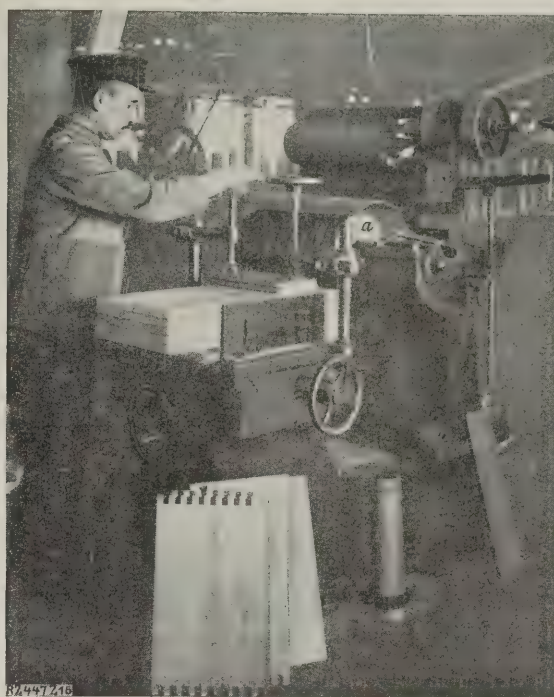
Zinkenfräsmaschine mit wagerecht liegender Fräswelle.
